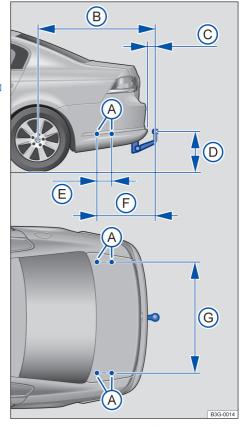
Dimensões e pontos de fixação para instalação posterior de um dispositivo de reboque (Passat).
